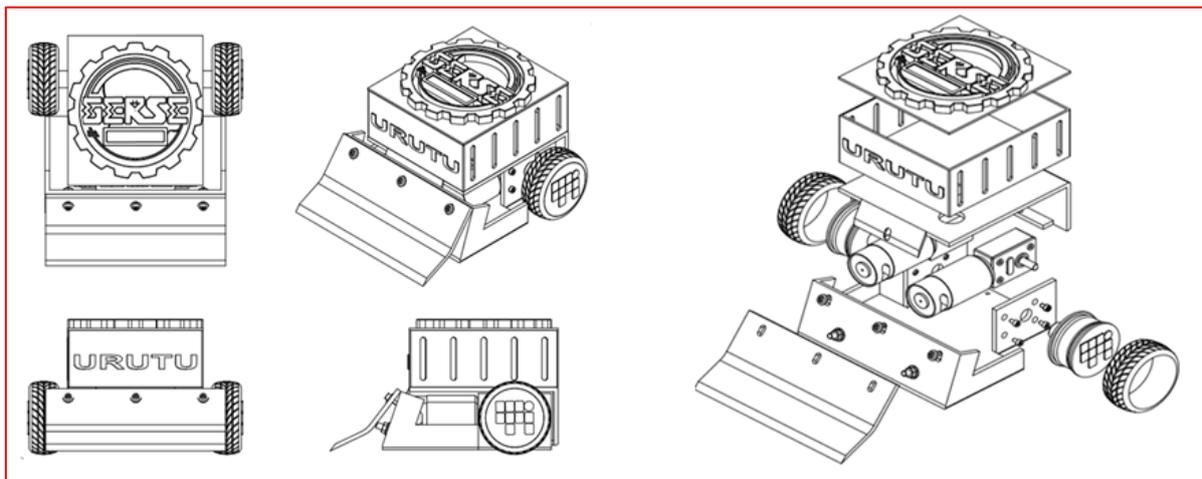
Projeção de vistas do robô Sumô e vista explodida.
